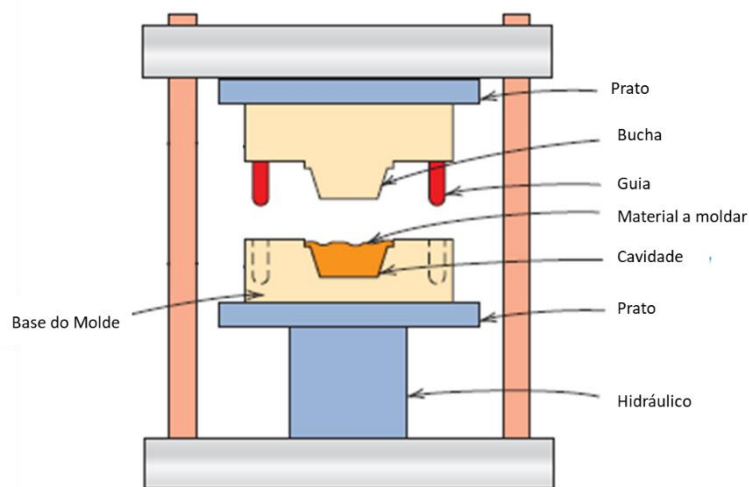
Esquema de moldação por compressão (adaptado de [10])
